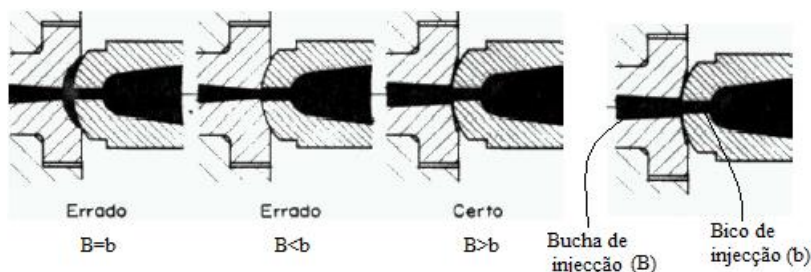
Contacto do bico de injeção (máquina injetora) com a bucha de injeção (molde) [9]
